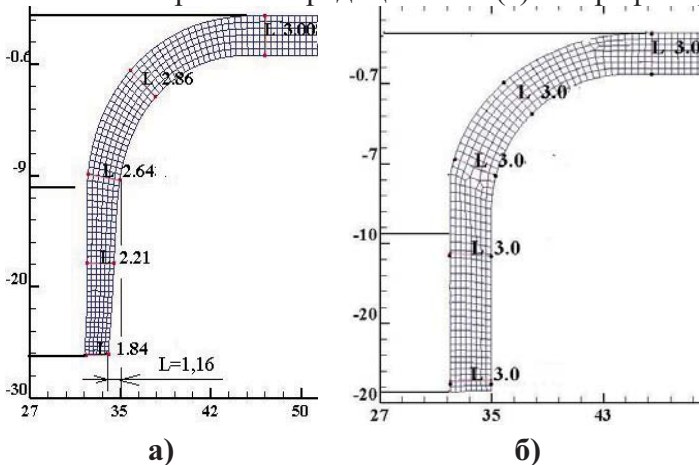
Форма и размеры отбортованной части: а- традиционная заготовка, б - спрофилированная заготовка (размеры в миллиметрах)
